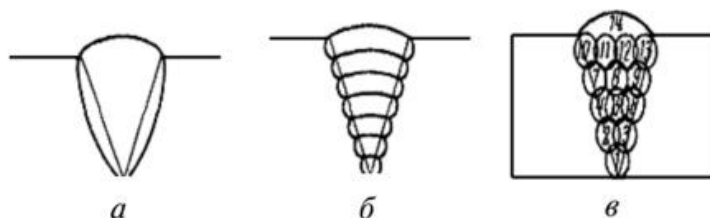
Схемы сварных швов: а – однопроходный; б – многослойный; в – многопроходный
